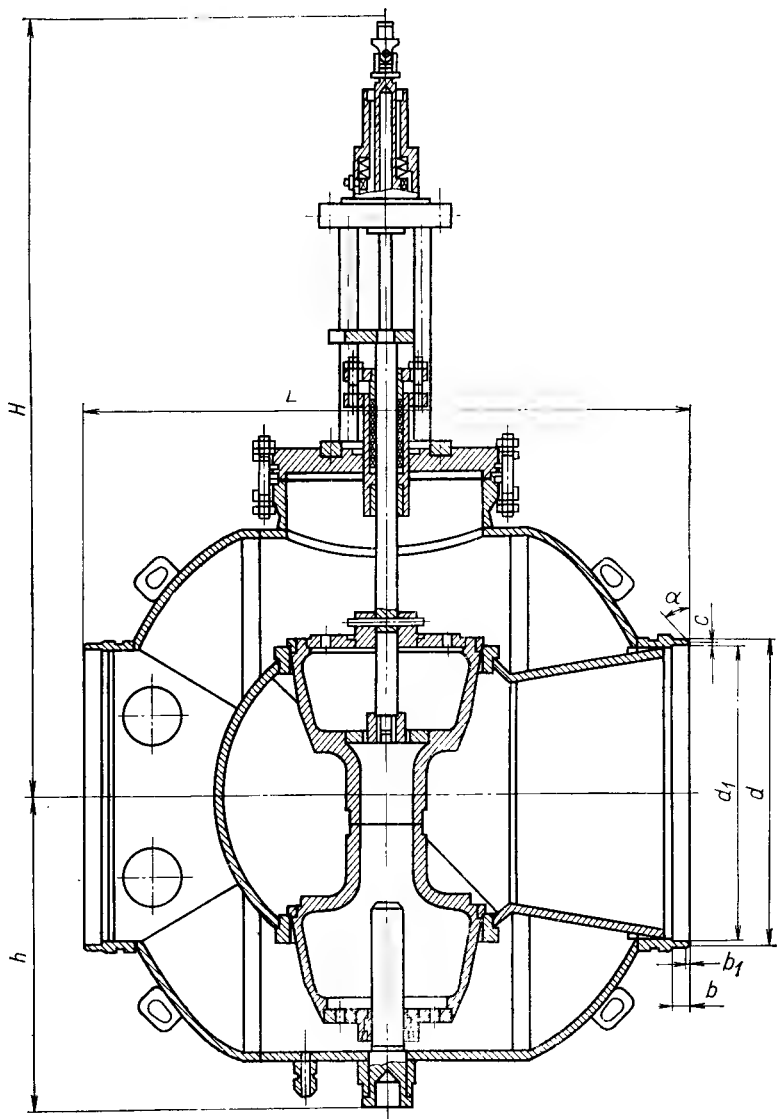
Регулирующий двухседельный клапан И 68051 на $p_y = 1,6$ МПа.
